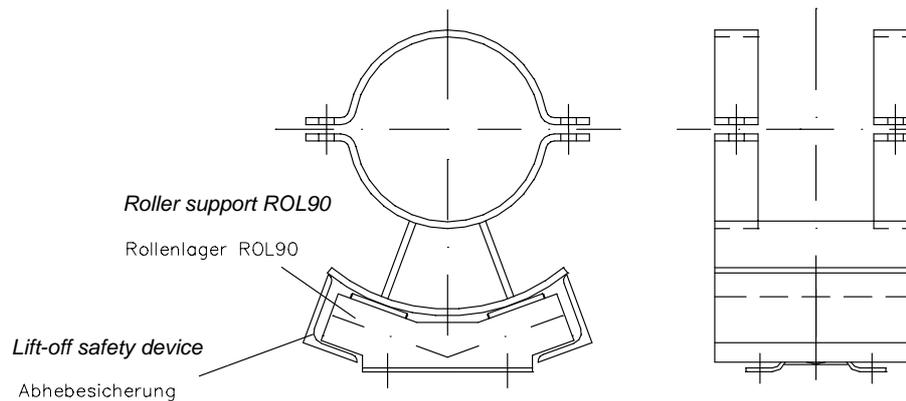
Abhebesicherung für Rollenlager ROL90
